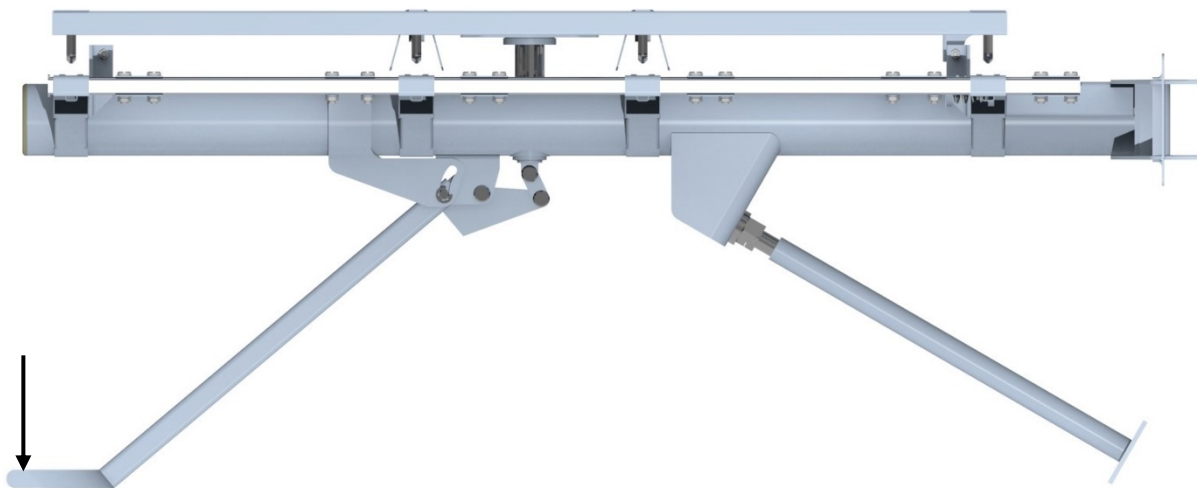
Mechanicky ovládaný otočný mechanismus v zajištěné poloze
